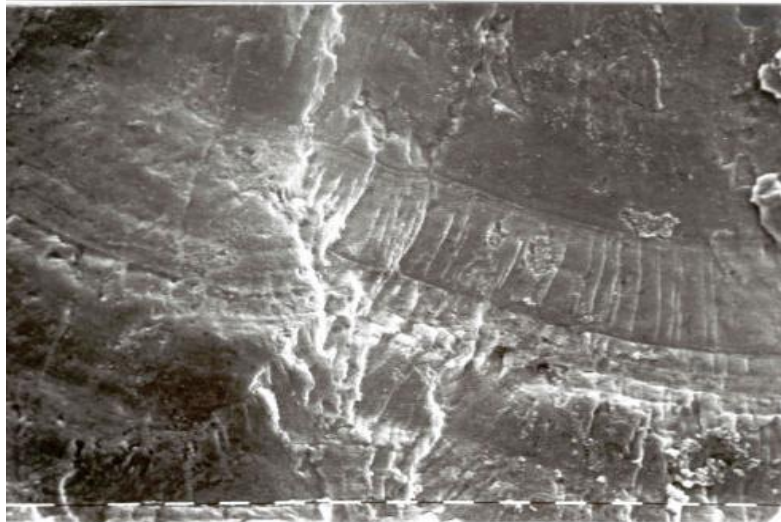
Detalle de una superficie de fractura por fatiga
